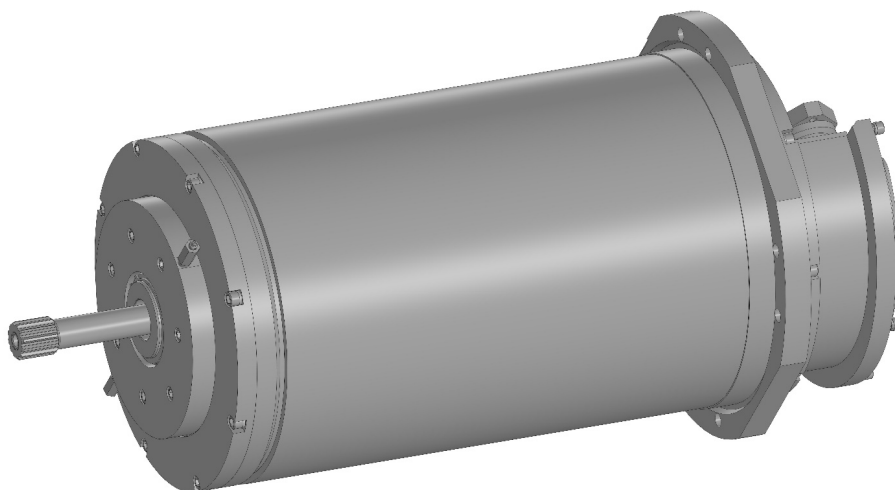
3D модель двигателя ЭКВ4,5-160-6
